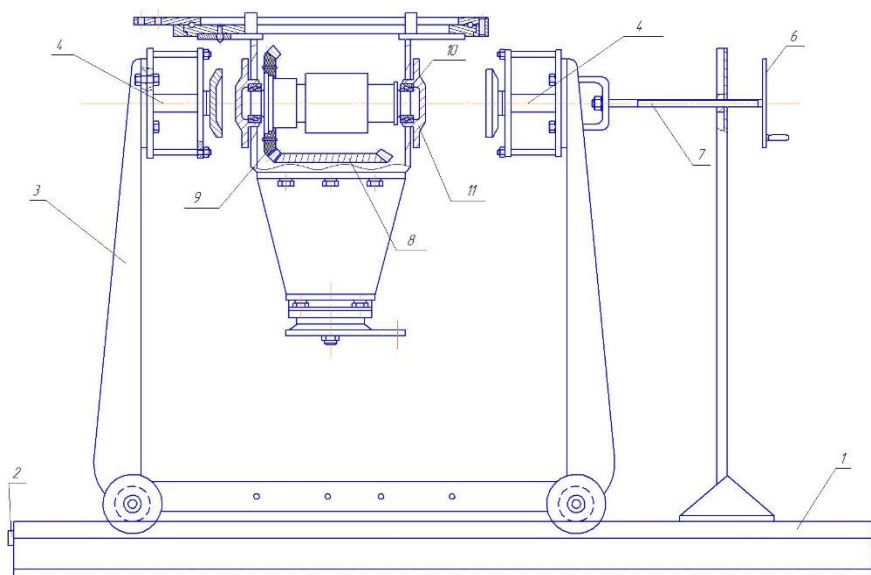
Стенд для установки положения спирально-конических шестерен главной передачи автомобиля: 1 – Опора; 2 – Планка; 3 – Тележка; 4 – Силовые цилиндры; 5 – Упоры; 6 – Маховик; 7 – Вал; 8 – Ведущая коническая шестерня; 9 – Ведомая коническая шестерня; 10 – Подшипники; 11 – Гнездо редуктора.
